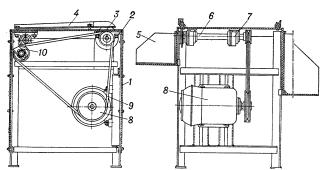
Калибровочная виноградниковая машина: 1 — рама; 2 — стол; 3 — фреза; 4 — калибровочный клин; 5 — бункер; 6 — вал фрезы; 7 — подшинник; 8 — электродвигатель; 9 — клиновидный ремень; 10 — натяжной ролик.
